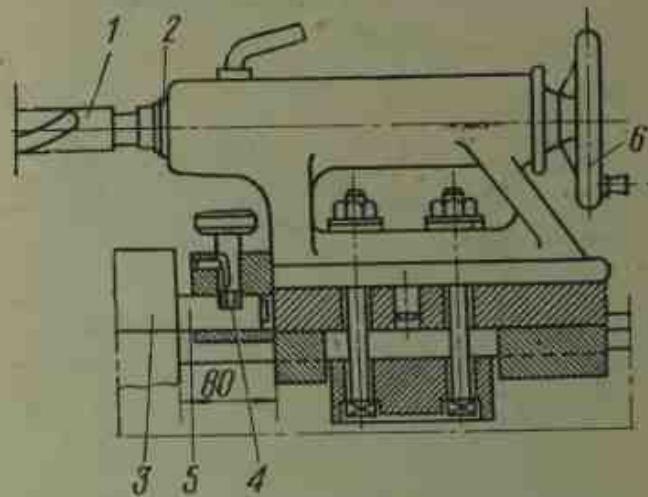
Приспособление для сверления отверстий с механической подачей на токарном станке:
